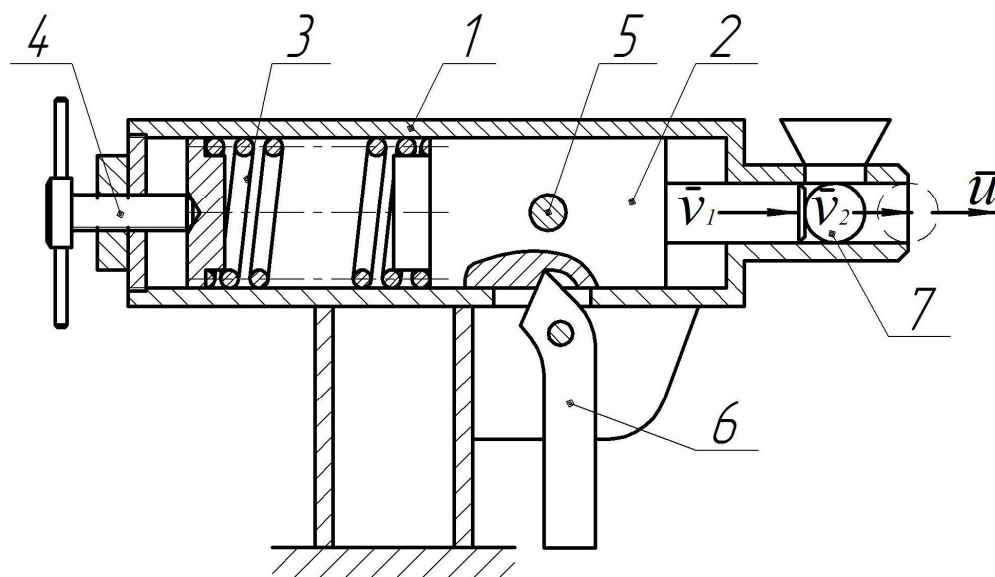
Схема устройства для проведения обработки единичного зерна сои ударной нагрузкой: 1 – корпус; 2 – плунжерный выталкиватель; 3 – рабочая пружина; 4 – винт регулировки степени сжатия рабочей пружины; 5 – элемент устройства взвода; 6 – стопорное устройство; 7 – зерно сои.
